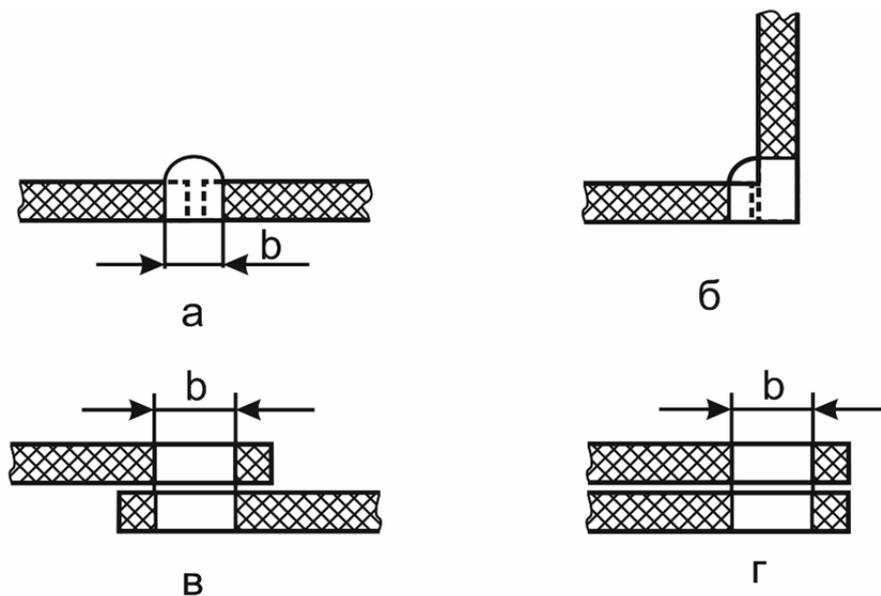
Сварные соединения полимерных пленок:
